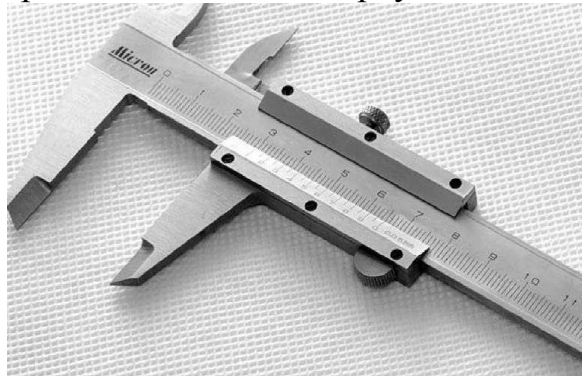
Прилад для вимірювання риб штангенциркуль
